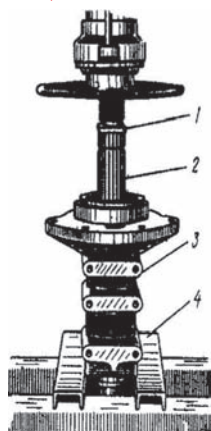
Выпрессовка шарикоподшипника с полуосью из рукава полуоси конечной передачи. 1 — пресс; 2 — полуось; 3 — рукав полуоси; 4 — подставка.
